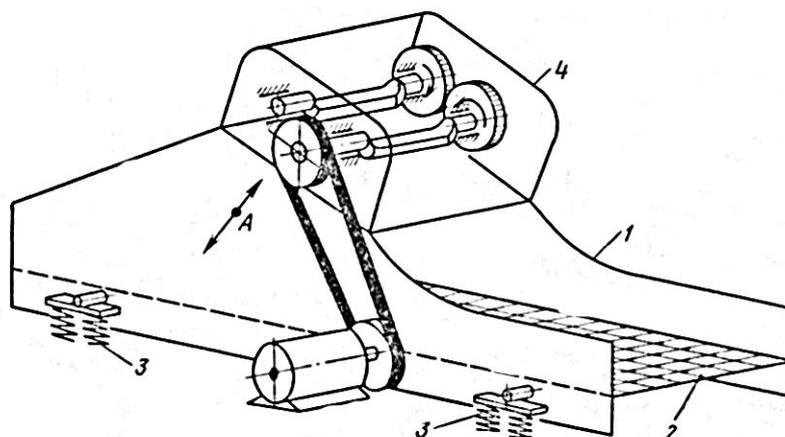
Схема самобалансного грохота с зубчатой передачей между валами:
